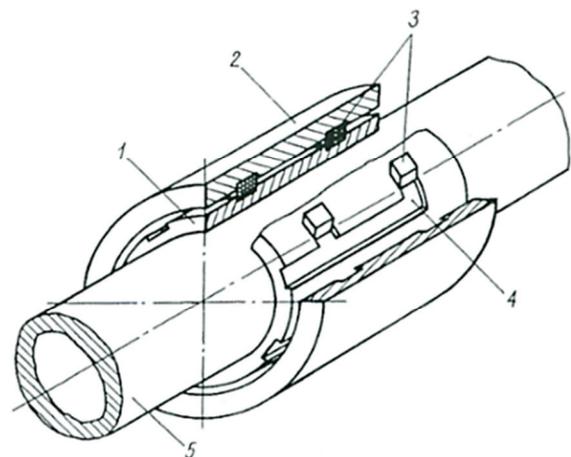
Схема подшипника с эластичным вкладышем: 1 – вкладыш с антифрикционным материалом; 2 – корпус подшипника; 3 – упругодемпфирующие элементы; 4 – пазы; 5 – вал
